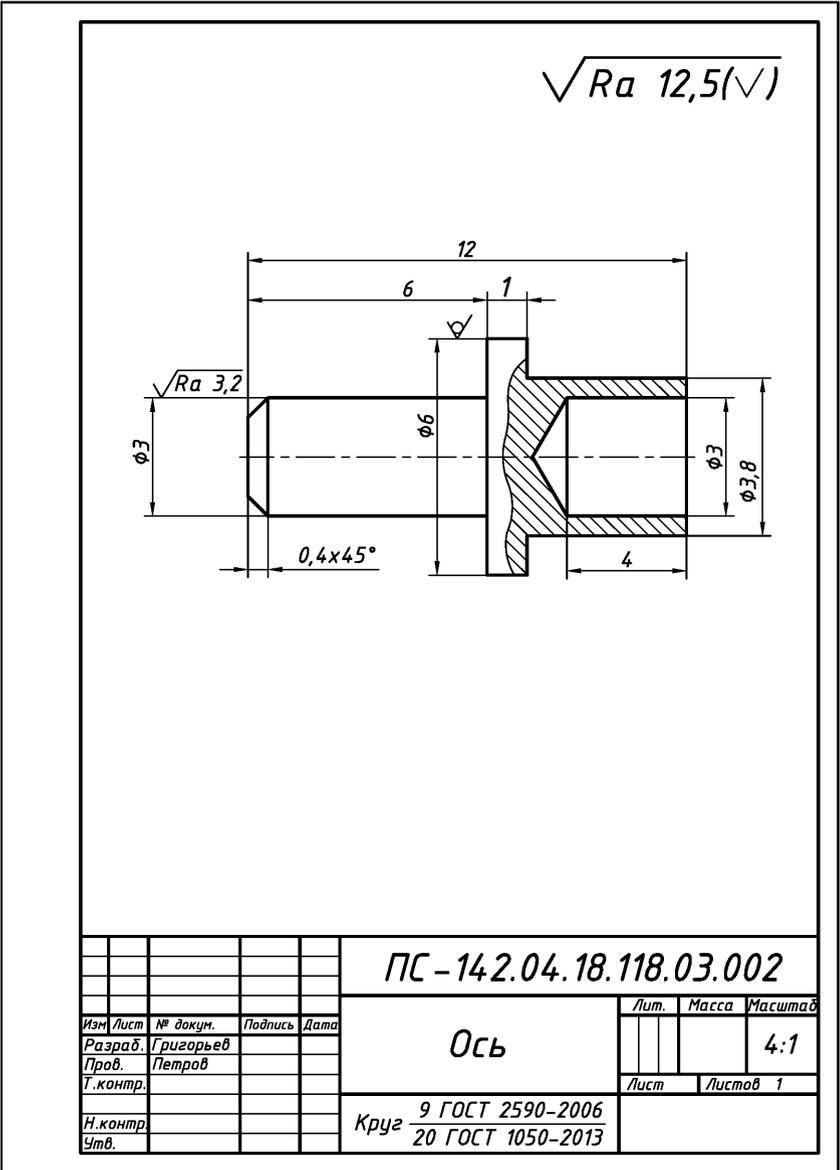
Оформление рабочего чертежа детали «Ось» сборочной единицы «Корпус» (рис. 1.72)
